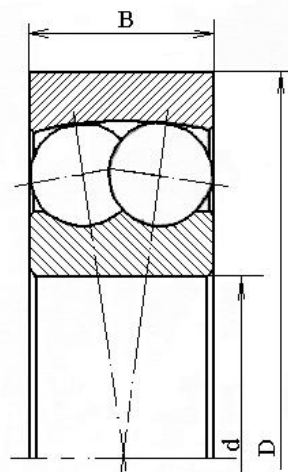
Подшипник шариковый радиальный, сферический, двухрядный, самоустанавливающийся
